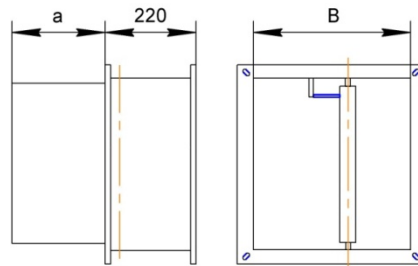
Установочные, габаритные и размеры внутреннего сечения клапана.
